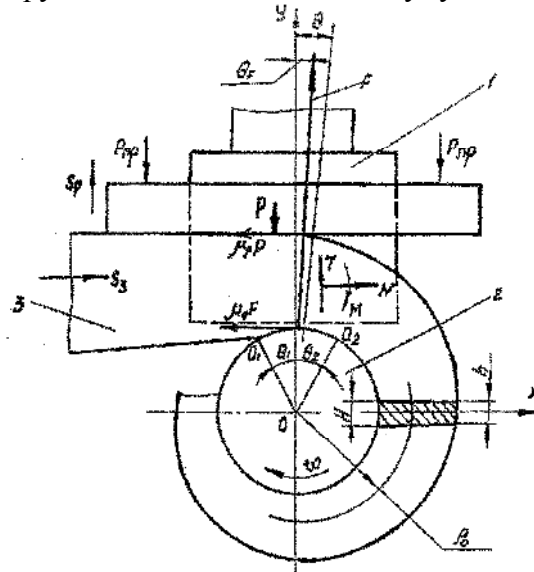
Розрахункова схема для визначення параметрів процесу навивання гвинтової заготовки конічної форми:
